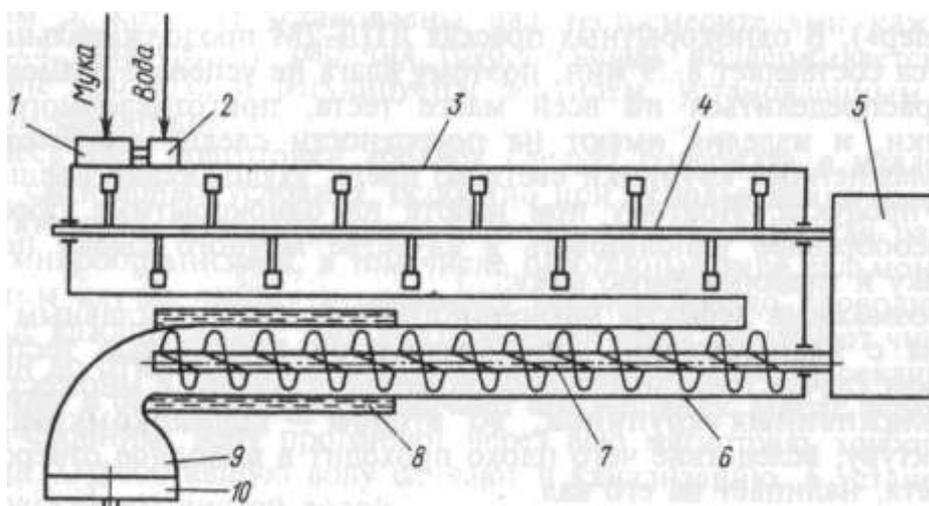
Макаронный пресс: 1 и 2 – дозаторы муки и воды; тестомеситель: 3 – корыта; 4 – вала с лопатками; прессующее устройство: 6 – шнековый цилиндр; 7 – шнек; 8 – водяная рубашка; 9 – прессовая головка; 10 – сменная матрица; 5 - привод
